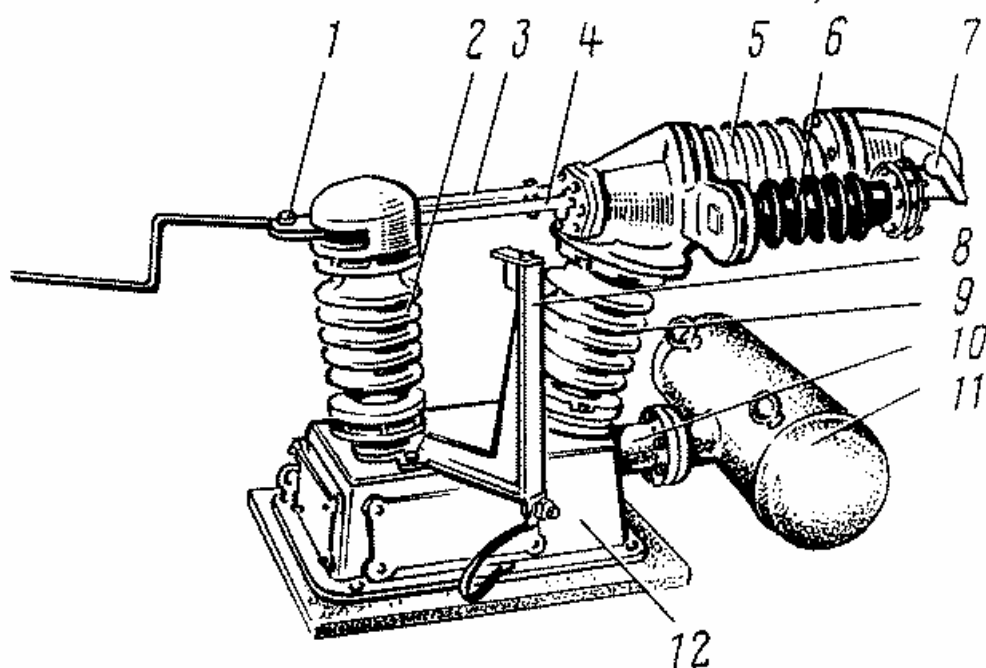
Воздушный выключатель ВОВ-25-4М
